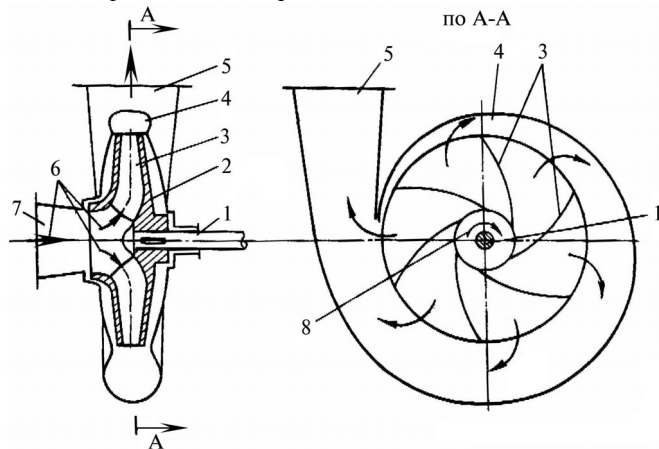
Схема одноступеневого (консольного) відцентрового насоса: 1 - вал; 2 - робоче колесо; 3 - лопаті робочого колеса; 4 - спіральна (равликоподібна) камера (корпус насоса); 5 - нагнітальний (дифузорний) патрубок; 6 - напрямок потоку рідини; 7 - усмоктувальний патрубок; 8 - напрямок обертання робочого колеса.
